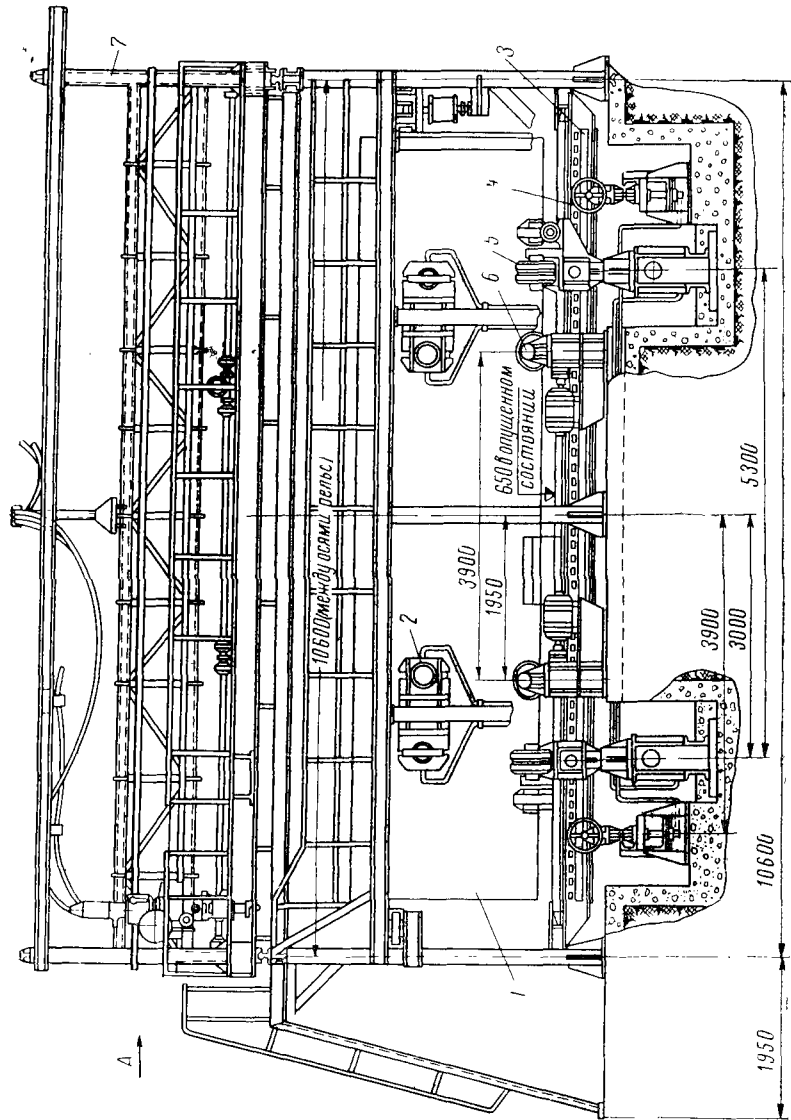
Стенд для сварки замыкающего стыка обечайки цистерны:
